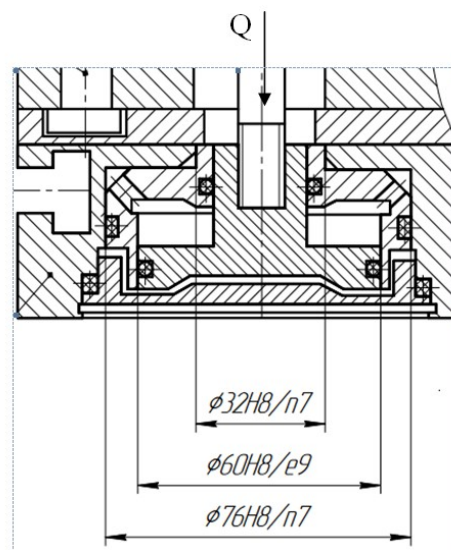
Загальний вигляд приводу пристрою
